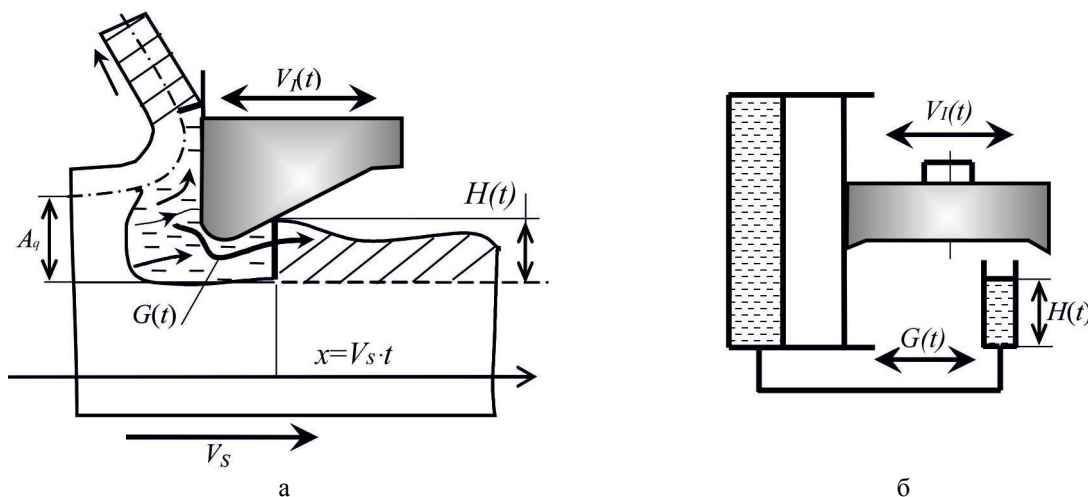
Формирование микропрофиля поверхности при относительном перемещении инструмента и заготовки: а – физическая модель процесса; б – эквивалентная гидравлическая схема процесса течения металла при формировании волнистой обработанной поверхности
